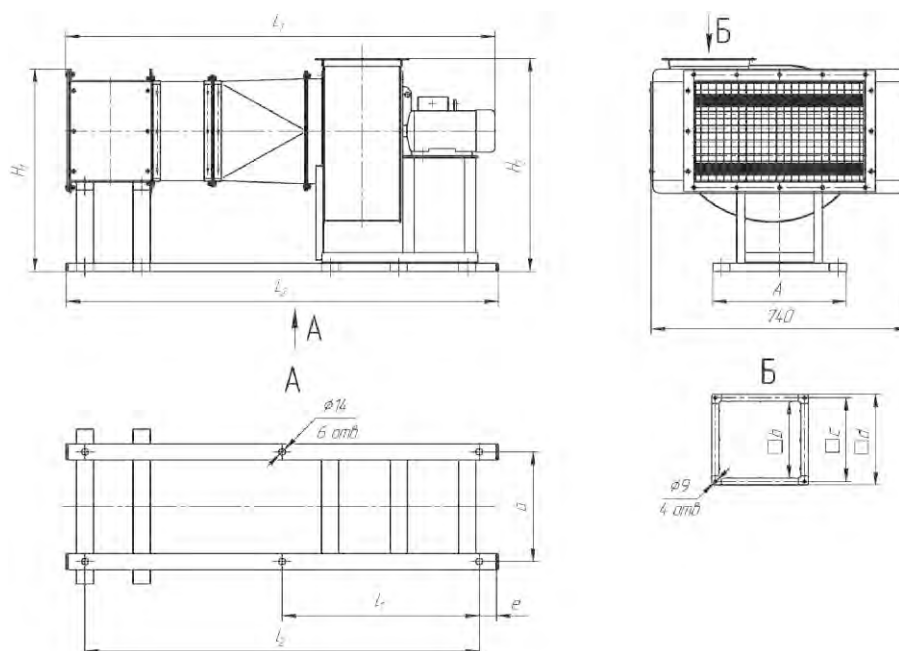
Габаритные и присоединительные размеры установок УВНЭ.
